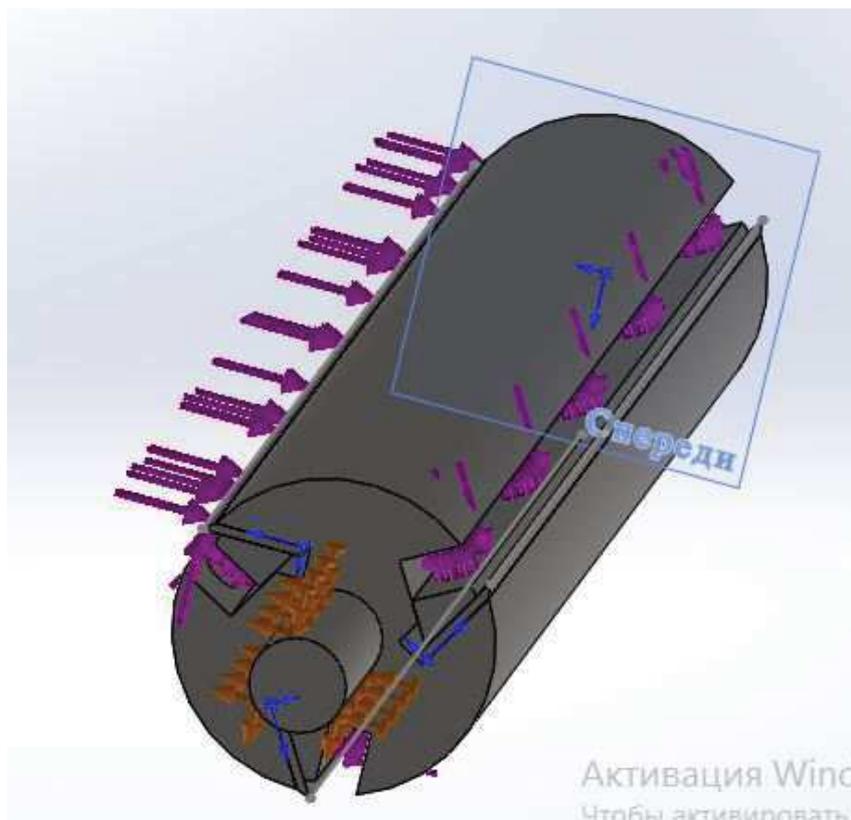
Анализ напряженного состояния фрезерного вала
